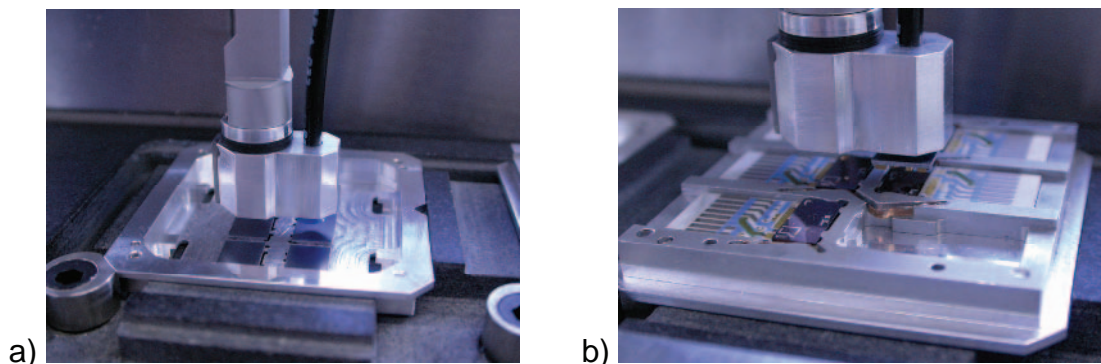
Saugnapfgreifer mit Werkzeugwechselschnittstelle; a) Greifer an Vertikalachse über geöffnetem und gedrehtem MOB-Werkstückträger; b) Montageaufgabe 3: MOB auf EOP
